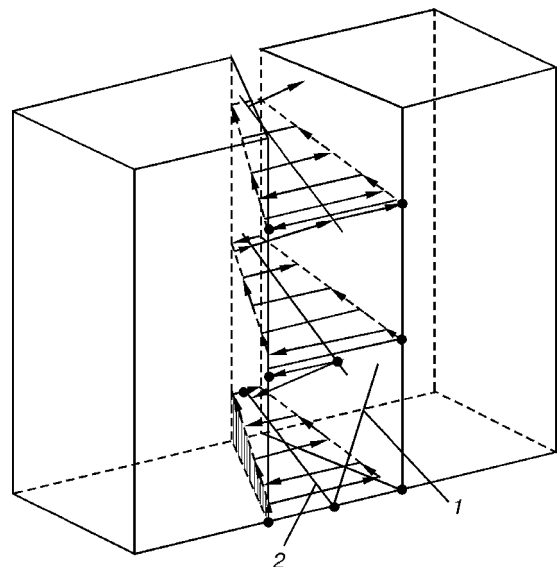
Схема сканирования сварочным инструментом при сварке по способу «поперечная горка»: 1 — исходное положение инструмента до начала сварки; 2 — биссектриса угла разделки кромок
